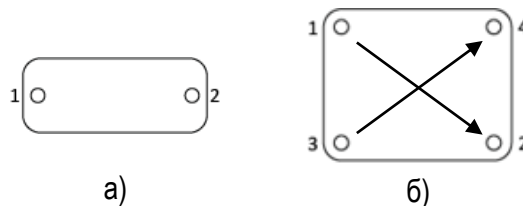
Последовательность крепления винтов для корпуса 34 мм (а) и для корпуса 62 мм (б).
